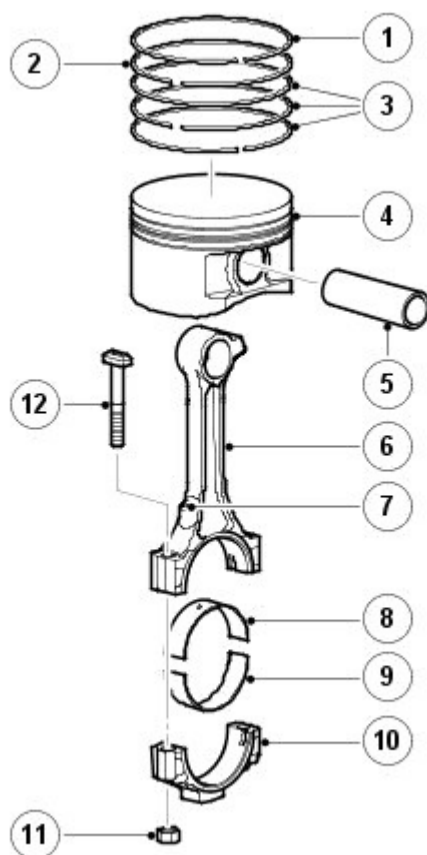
Поршень и шатун бензинового двигателя 4.0L V6
